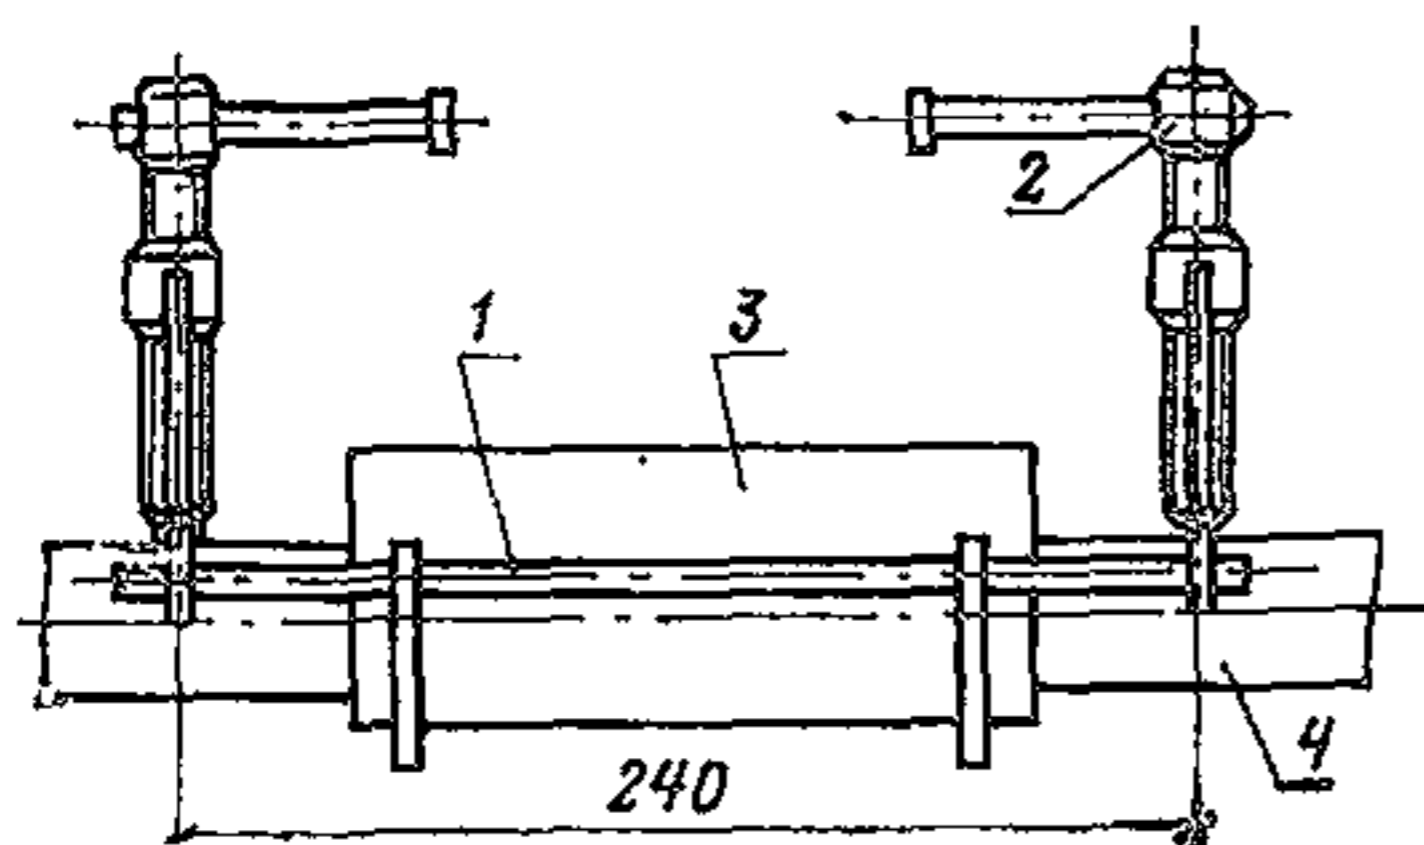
Приспособление для удержания желобчатой подкладки при сварке стыковых соединений стержней (конструкция ЦНИИОМТП)
